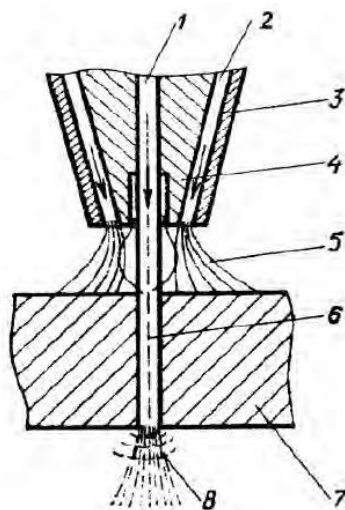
Кислородная резка: 1 – канал для кислорода; 2 – канал для ацетилена; 3 – наружный мундштук; 4 – внутренний мундштук; 5 – подогревающее газовое пламя; 6 – струя режущего кислорода; 7 – разрезаемый металл; 8 – шлак
